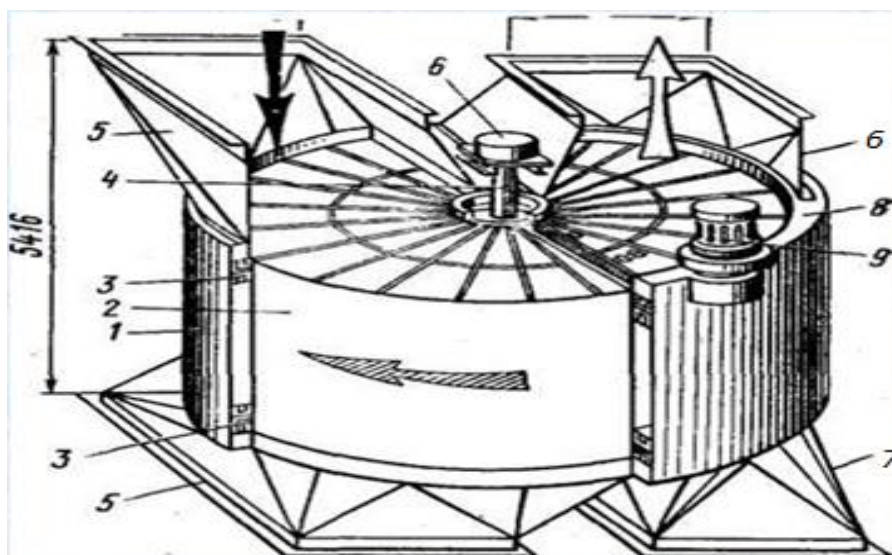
регенеративный вращающийся воздухоподогреватель: 1 – наружный кожух; 2 – ротор; 3,8 – наружное и радиальное уплотнения ротора; 4- вал ротора; 5,7 – коробка для газа и воздуха; 6- верхний подшипник; 9 – электродвигатель с редуктором
